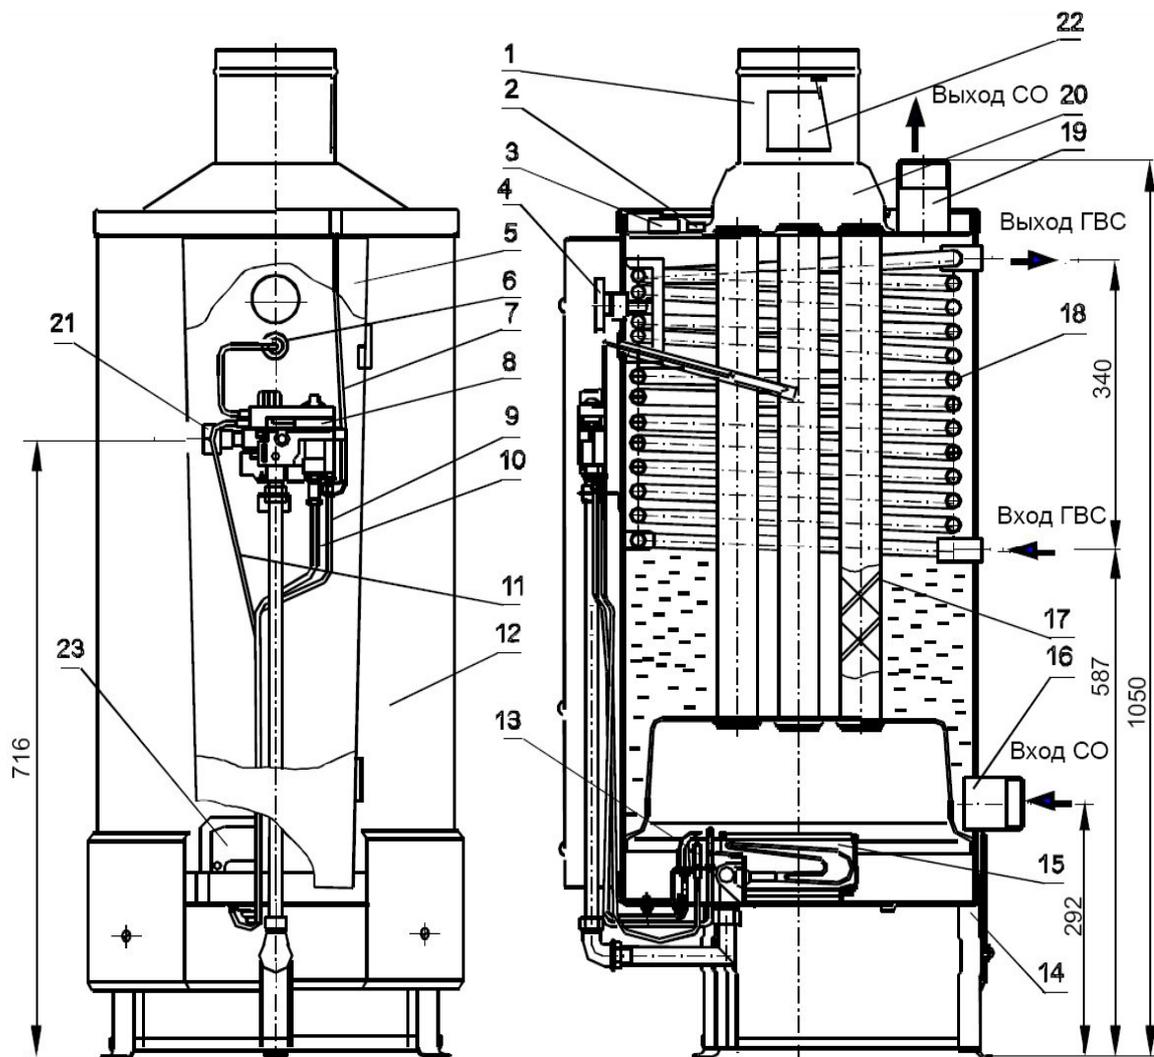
в. Котел отопительный газовый бытовой напольный комбинированный КОГВК-17,4 Honeywell, КОГВК-23,2 Honeywell
